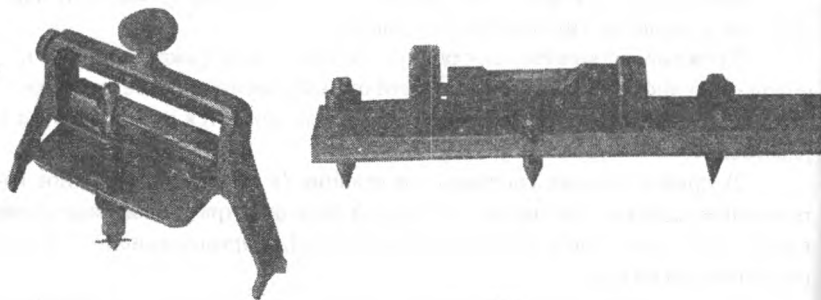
Приспособления для определения верхних образующих цилиндрических поверхностей
